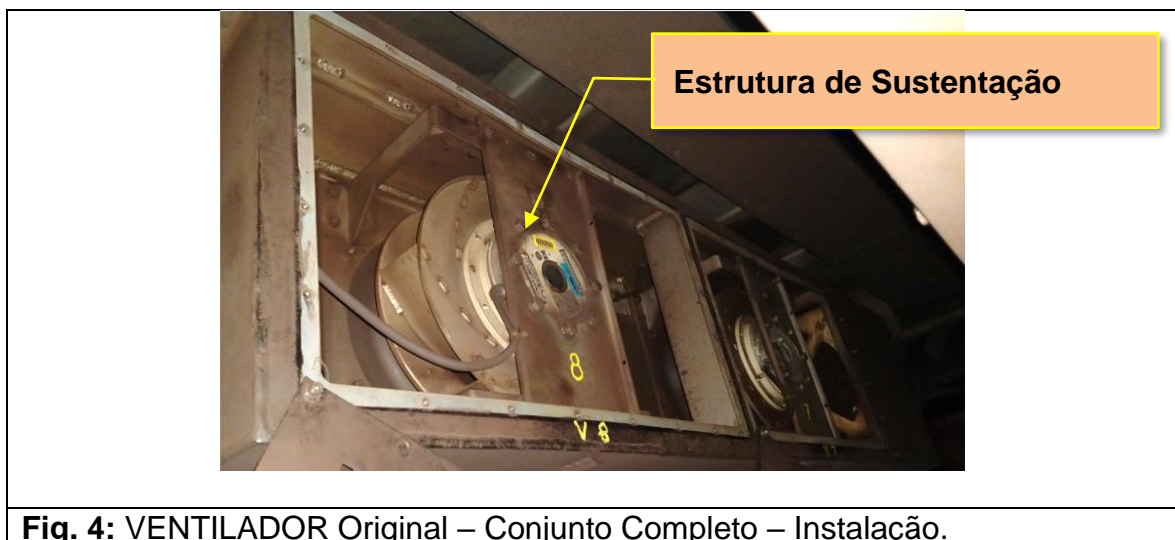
VENTILADOR Original – Conjunto Completo – Instalação.
